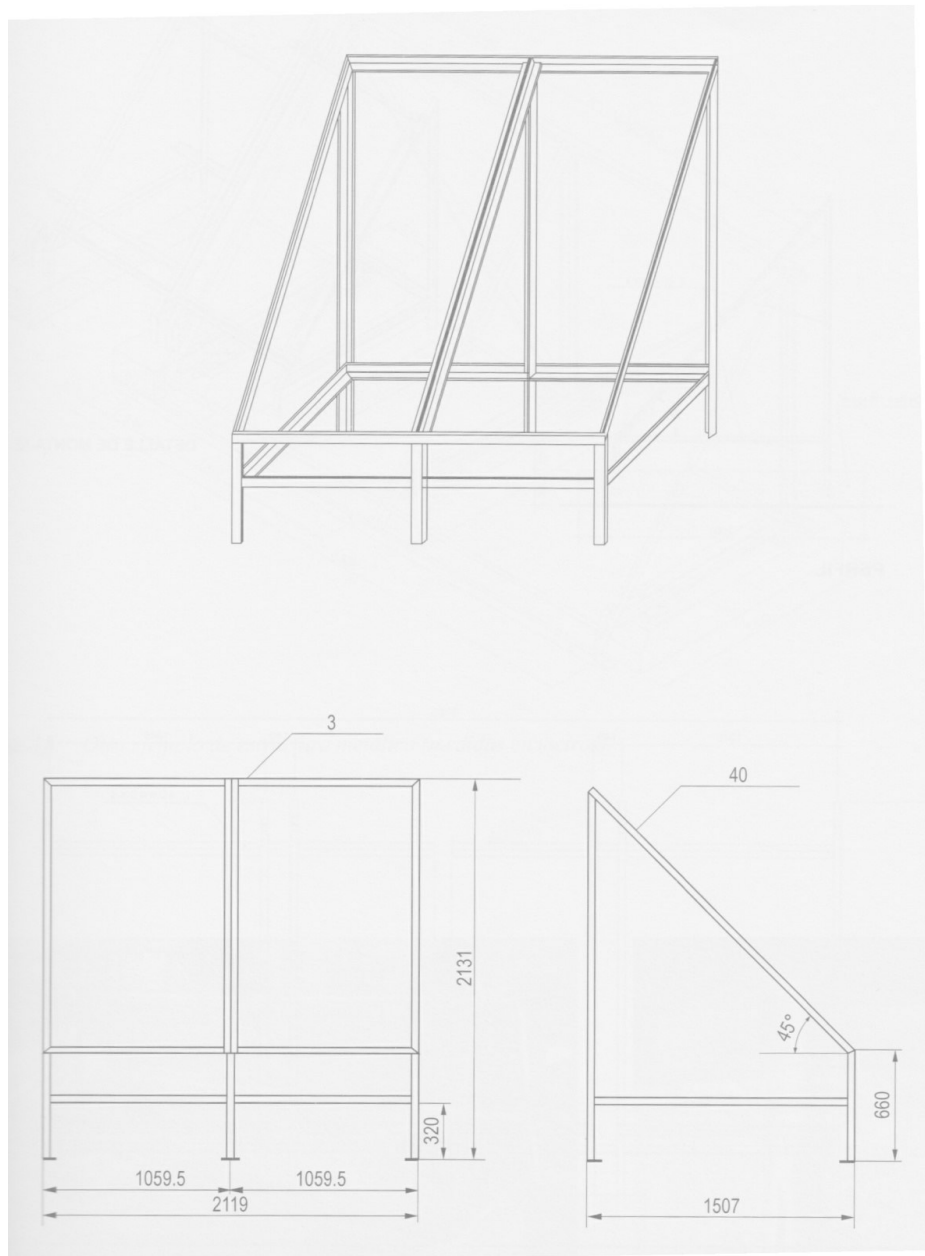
Típica estructura metálica para paneles fotovoltaicos, en perspectiva, alzado y perfil, mostrando sus medidas en milímetros (fuente: CENSOLAR)
